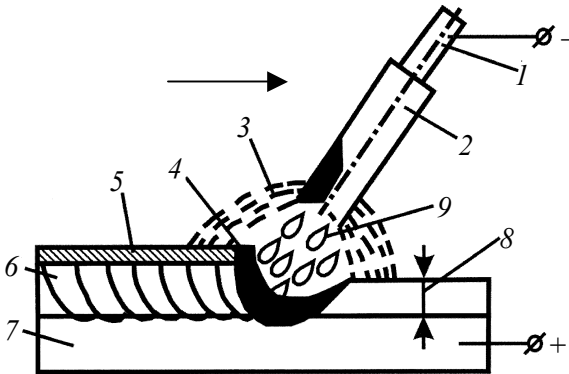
Ручне дугове зварювання металевим електродом з покриттям (стрілкою вказаний напрям зварювання):
